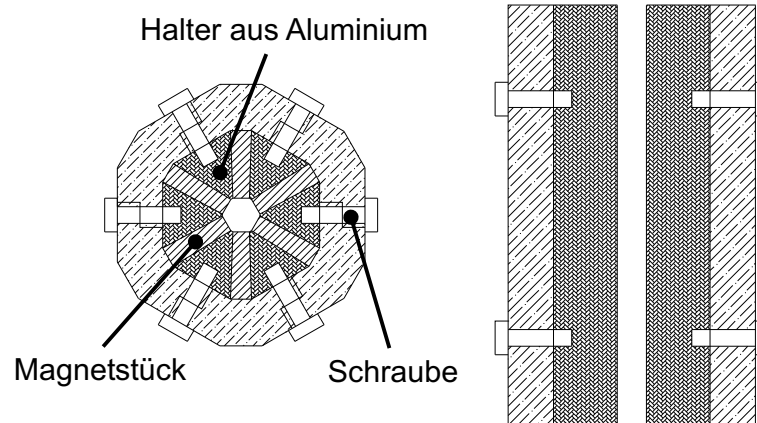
Der Hexapolmagnet in der Draufsicht (links) und in der Seitenansicht (rechts). Links sind die 6 Magnetstücke zu erkennen, die von den dreieckigen Aluminiumstücken und dem Feldrückführungsjoch gehalten werden. Die Länge des Magneten beträgt 10 cm. Der Innendurchmesser beläuft sich auf 8 mm.
